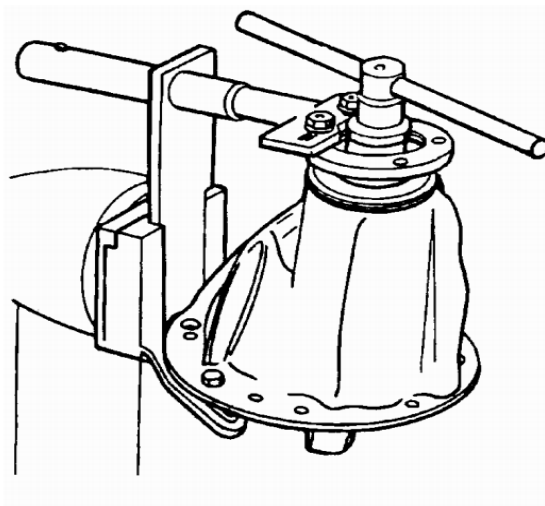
Установка по ремонту редукторов “Ач 22204”
